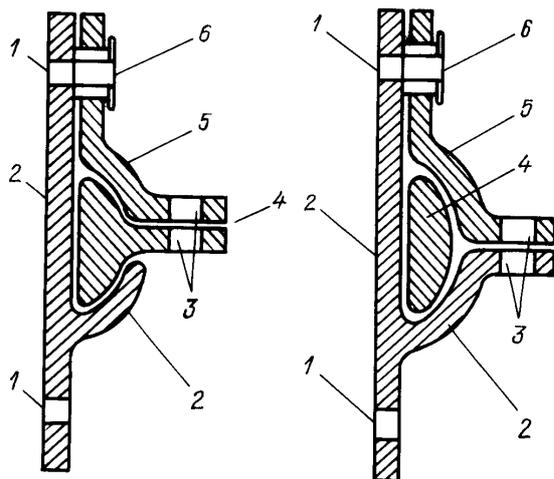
Приспособления для наложения таможенных печатей и пломб:
